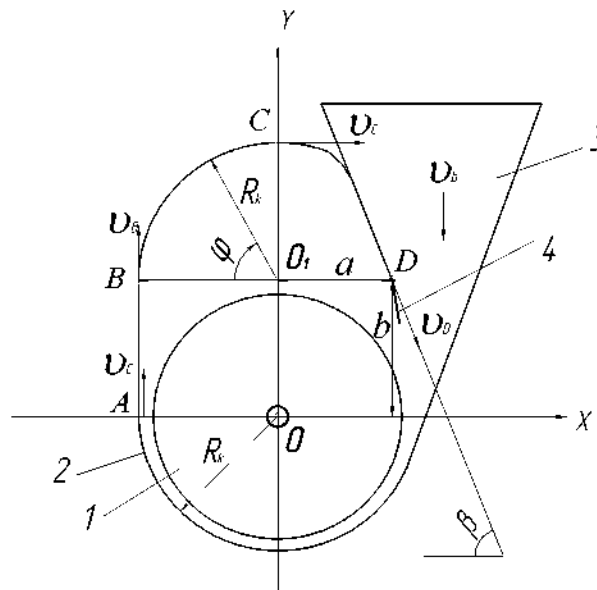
Схема до визначення форми робочої поверхні кожуха змішувача у зоні завантаження: 1 – гвинт; 2 – кожух; 3 – бункер-дозатор; 4 – шторка.
